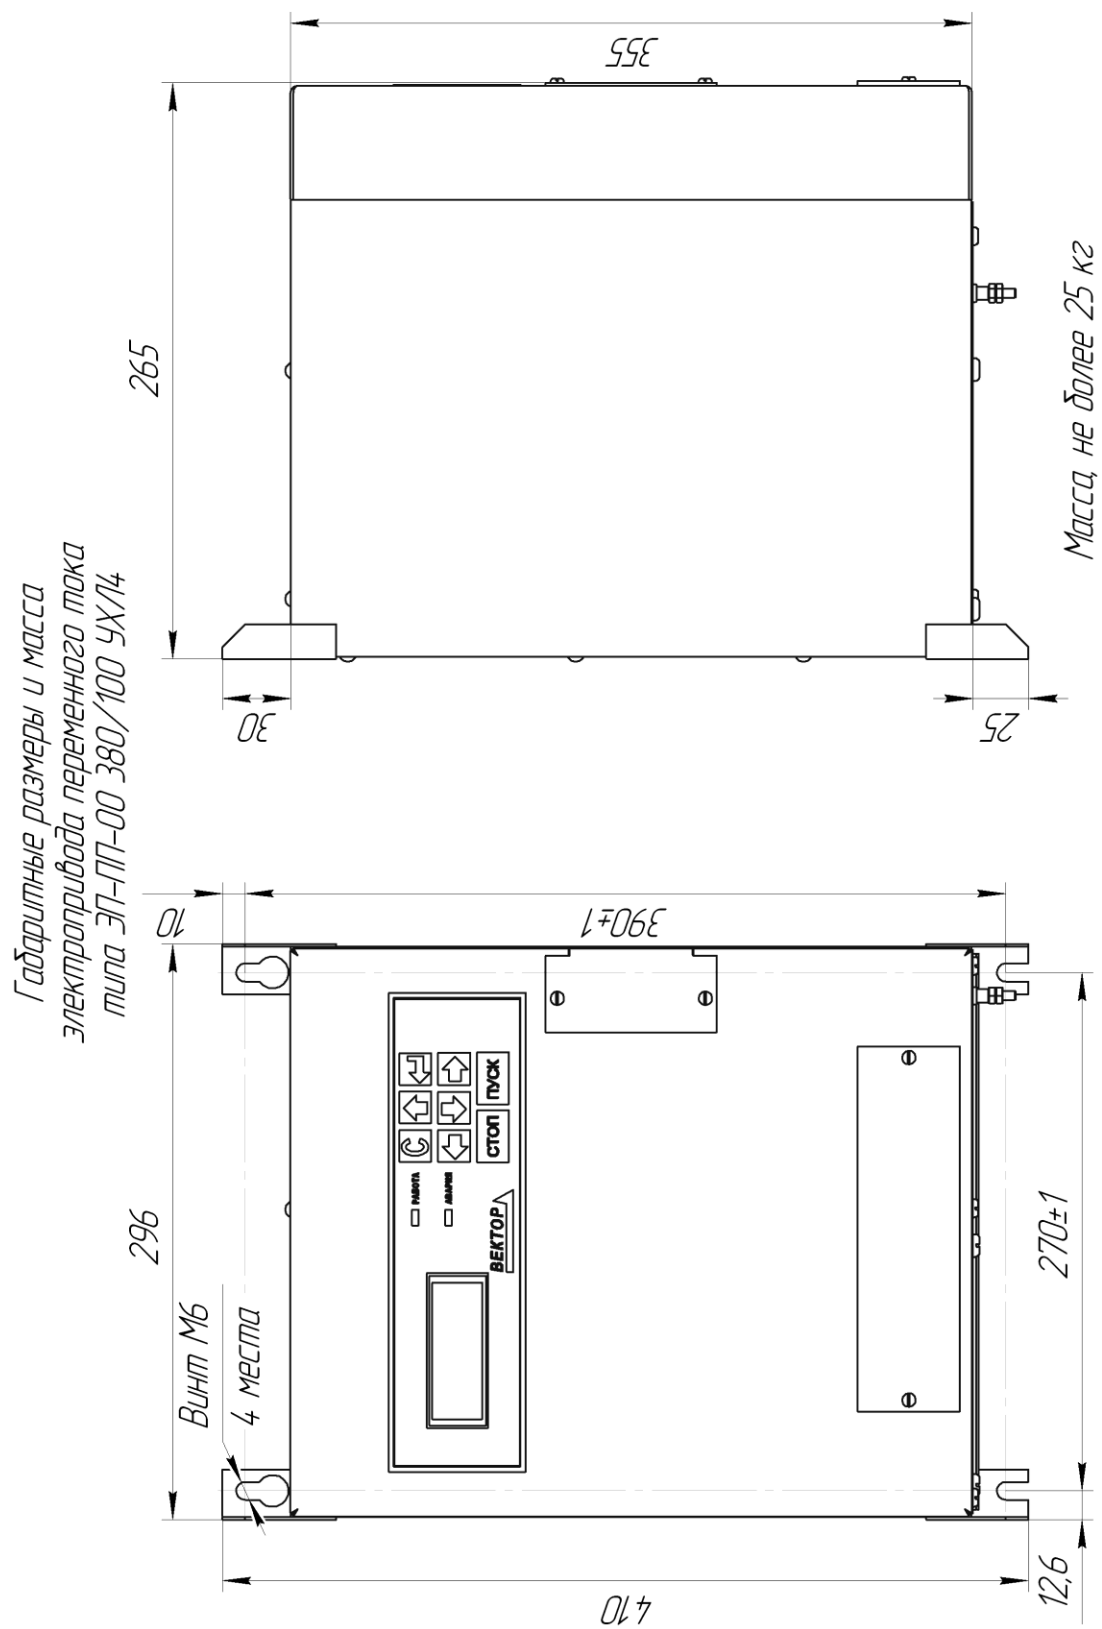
Габаритные и установочные размеры ЭП-ПП-00 380/100
